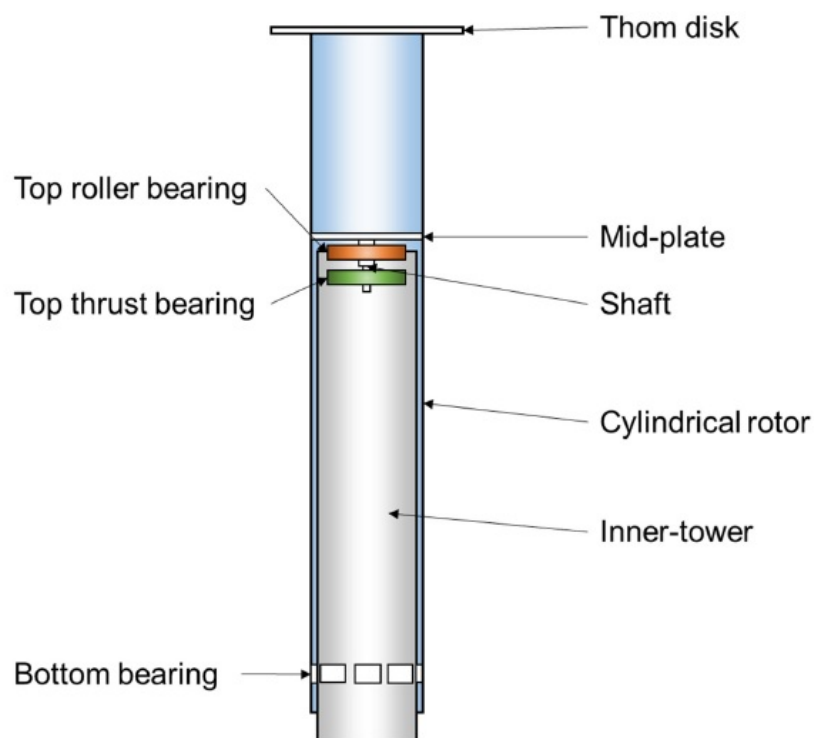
Поперечний переріз конструкції вітрила-ротора
